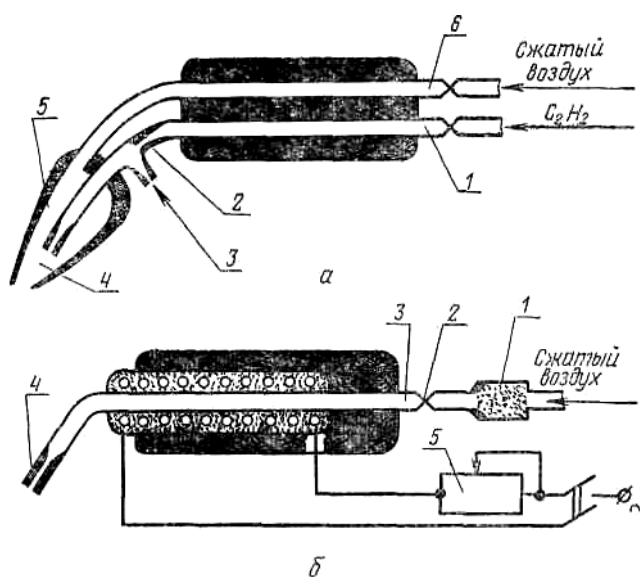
Схема горелок для сварки термопластов горячими газами:
